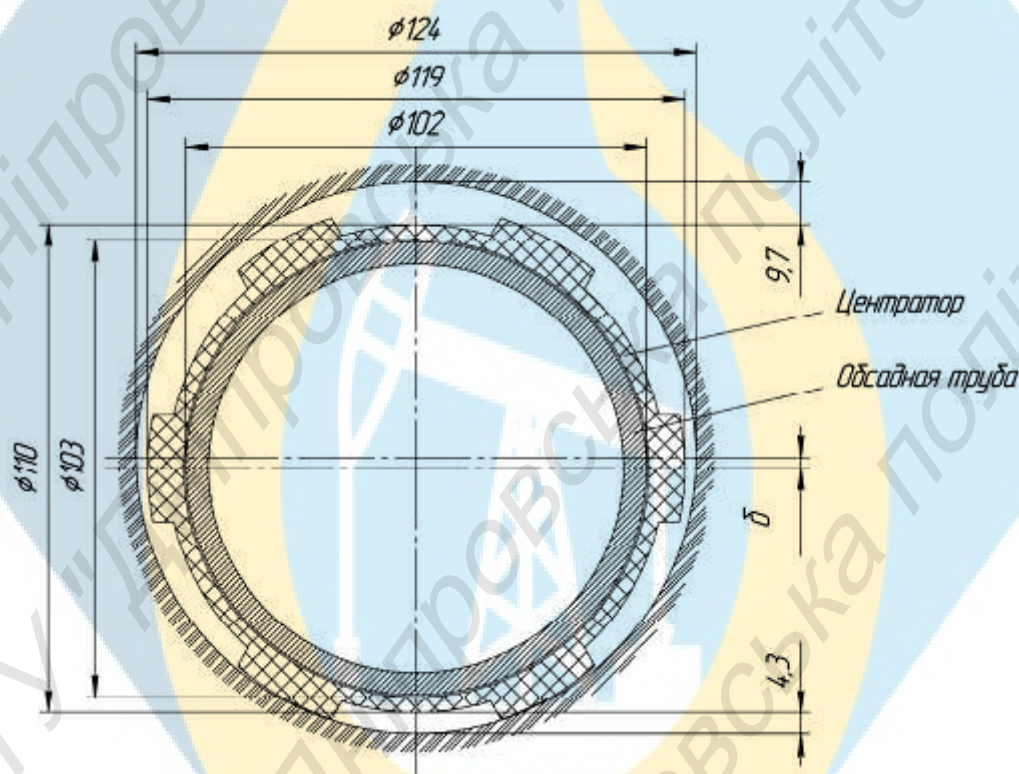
Розташування центратора і обсадної колони в свердловині
